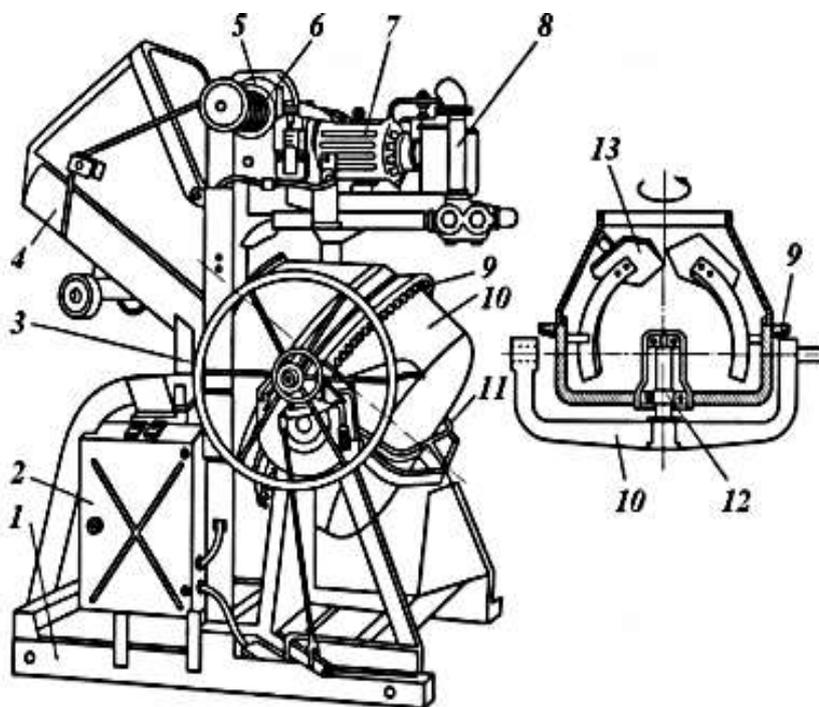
Опрокидывающийся гравитационный смесительный барабан: 1-рама; 2-электрооборудование; 3-штурвал опрокидывания барабана; 4- скиповый ковш; 5- червячный редуктор; 6-подъемник ковша; 7-двигатель; 8-водяной дозатор; 9-зубчатый приводной венец; 10-барабан; 11-траверса; 12-ось вращения барабана; 13-перемешивающая лопасть.
